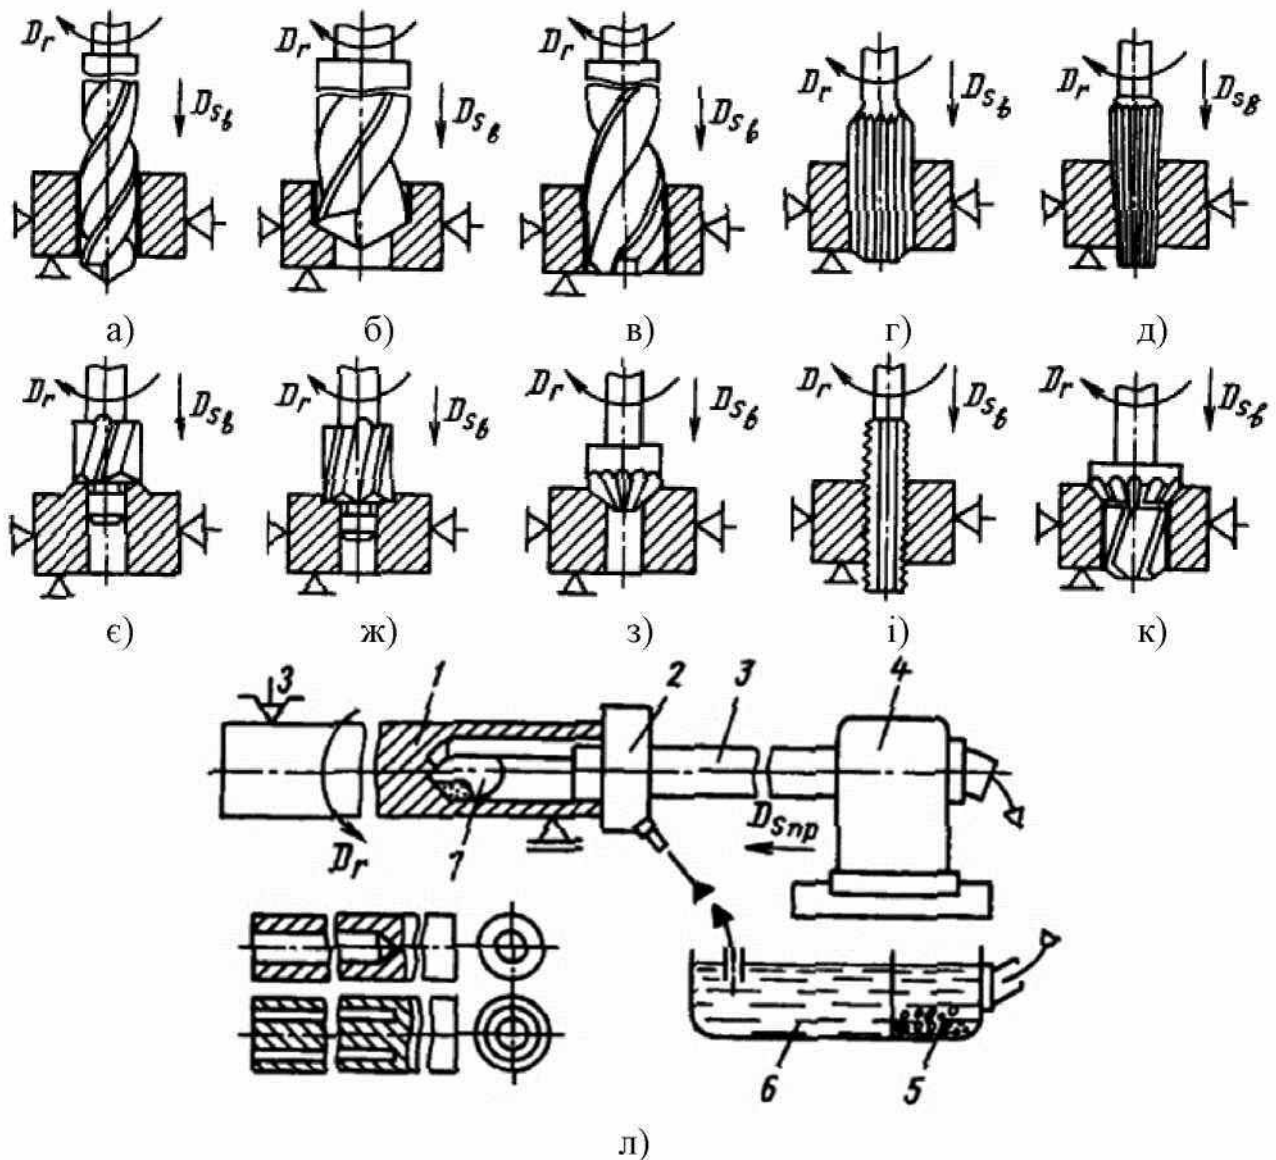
Схеми обробки заготовок на свердильних верстатах
